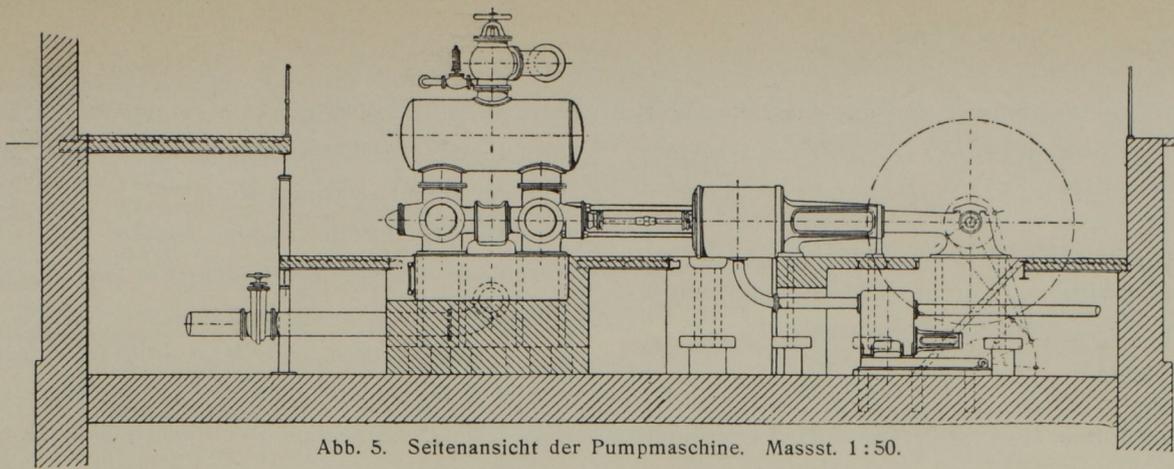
Seitenansicht der Pumpmaschine. Masst. 1:50.
